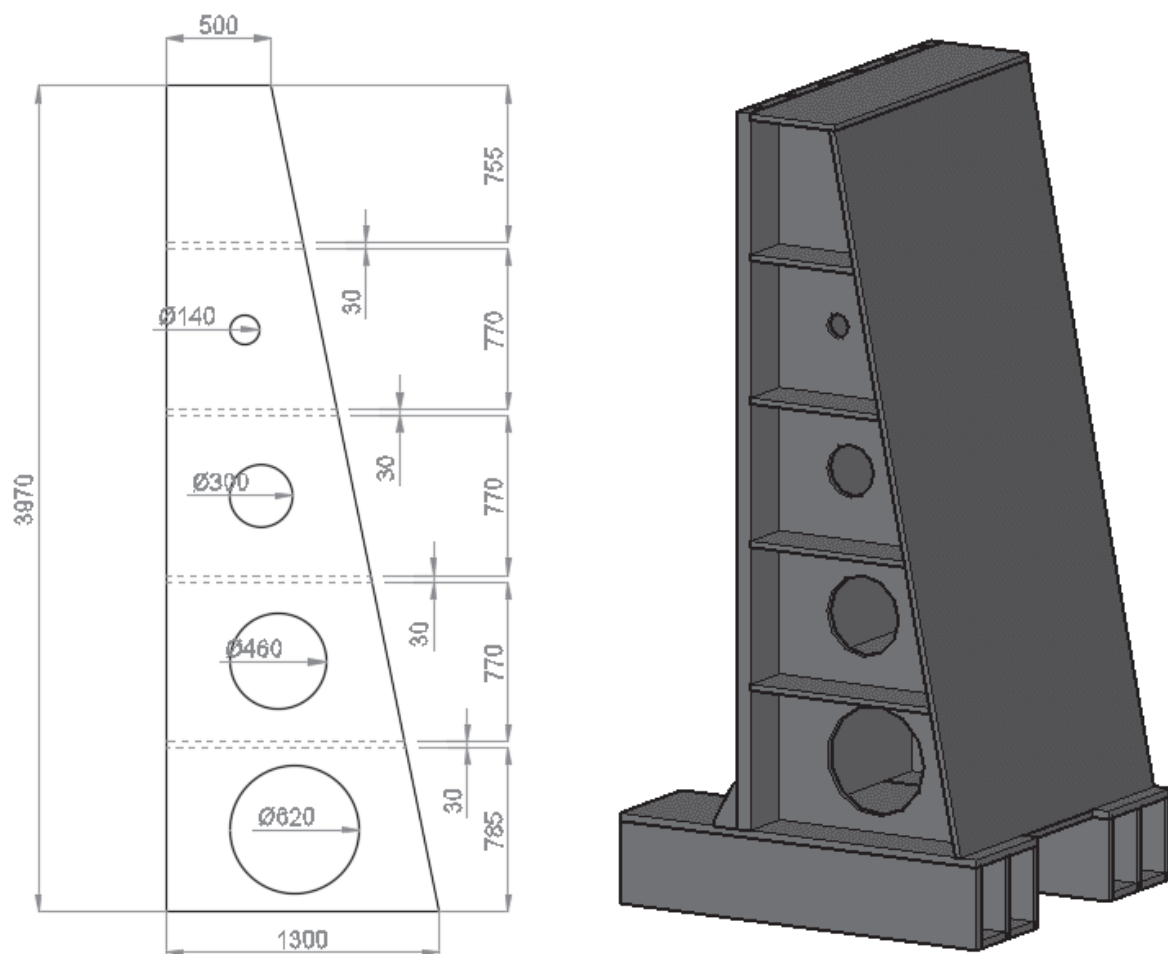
Schematizzazione lastra di costolatura trapezoidale (unità di misura in mm) e vista tridimensionale della struttura modello N°2 tipo A
